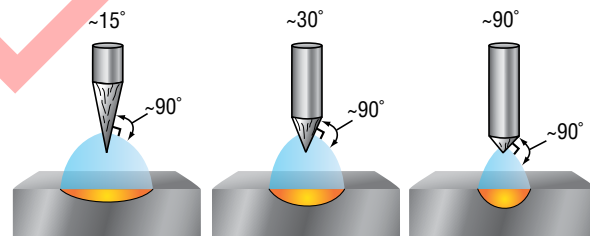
Los efectos en el ancho y profundidad de penetración del cordón de soldadura con ángulos incluidos variantes
